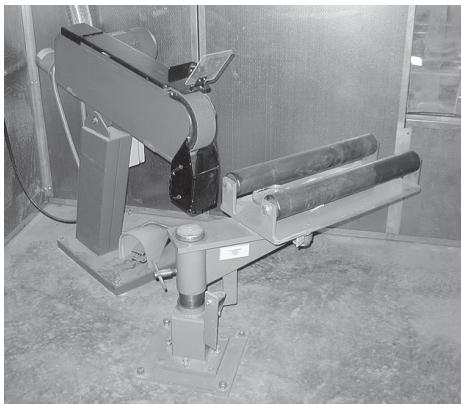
Шлифовальное устройство для подготовки сваренных поверхностей
